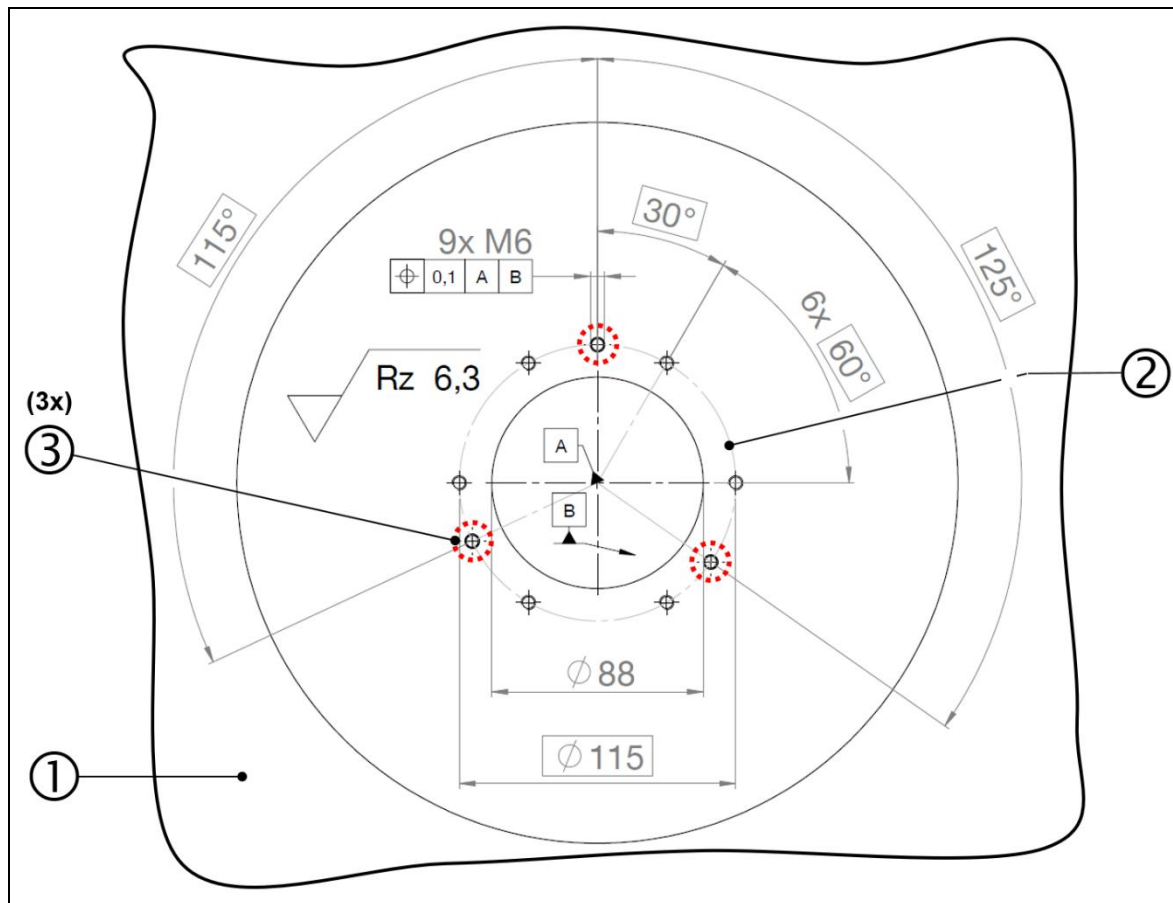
Esquema de taladros en la tapa de la pared del motor, BEAROMOS® 2020
